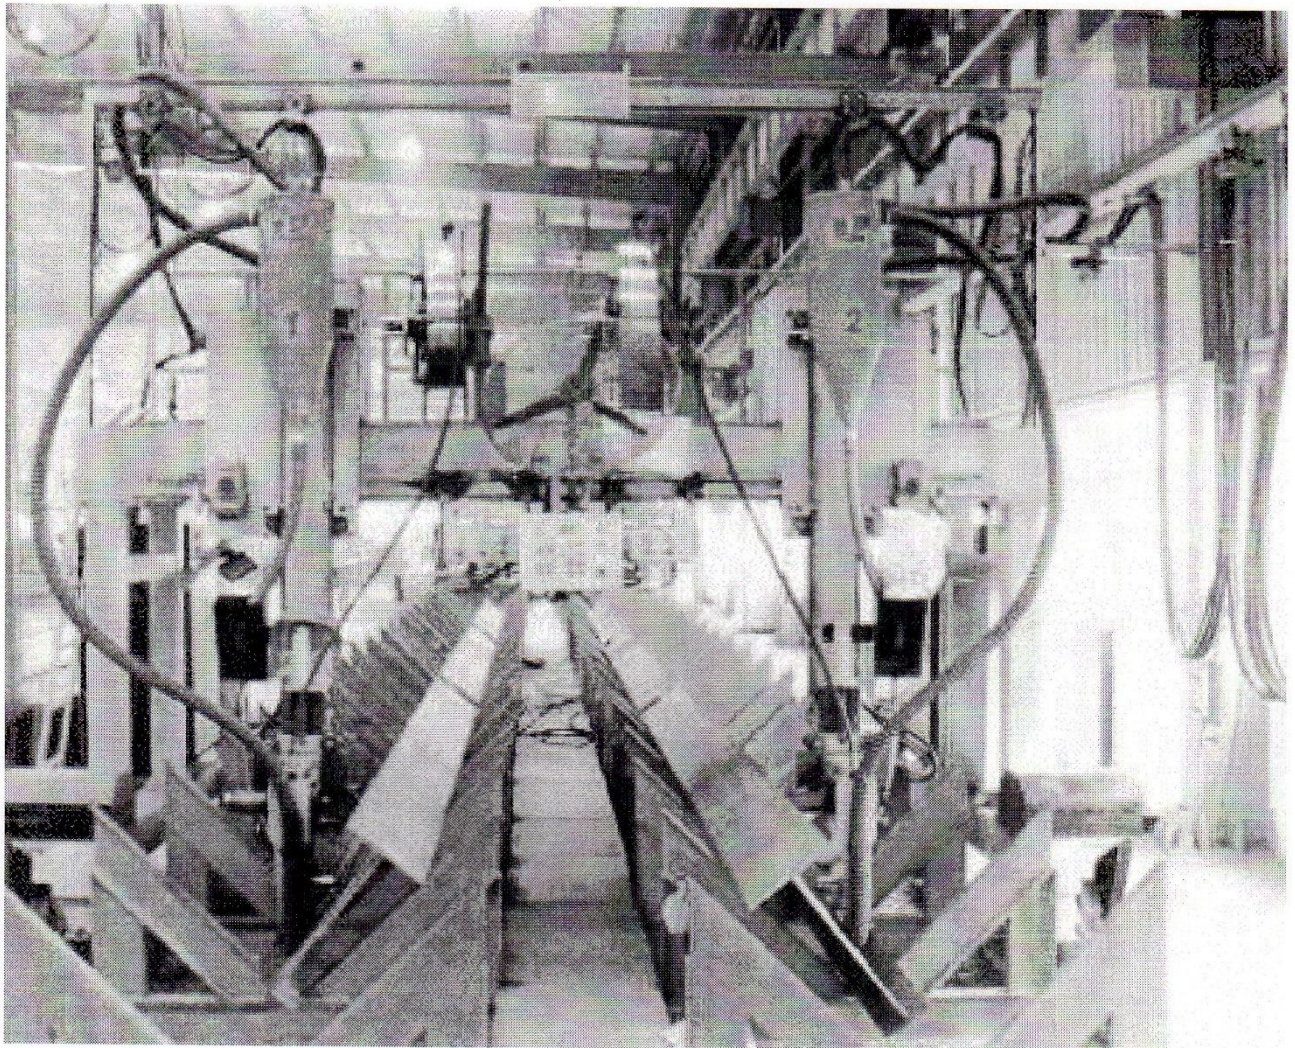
Установка для зварювання двотаврових балок портального типу
